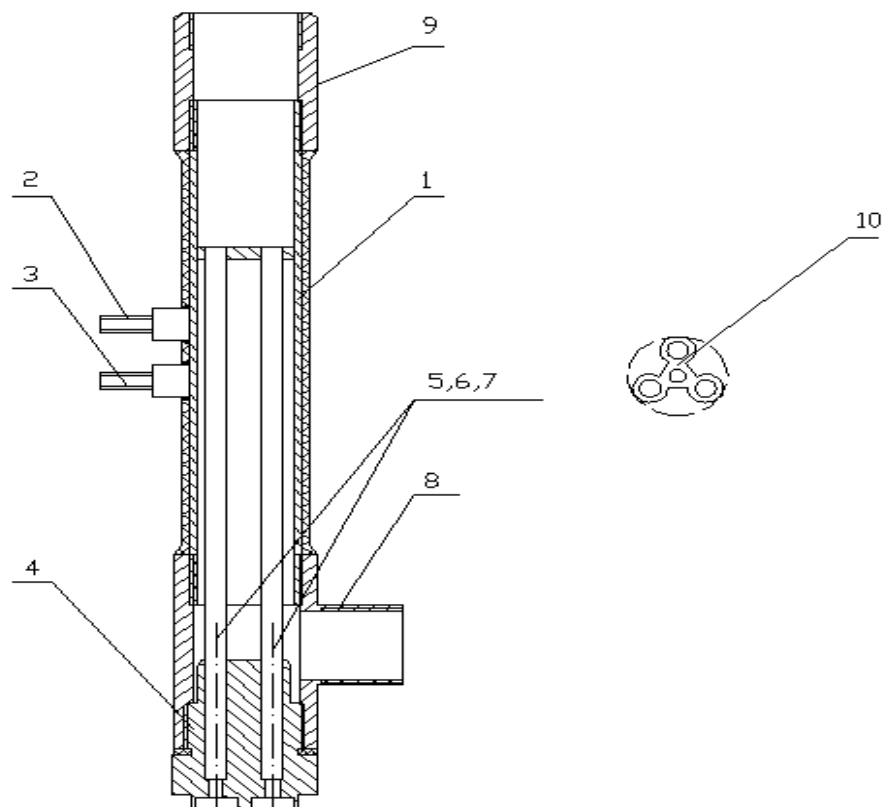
Пристрій електродний для пароутворення: 1 – корпус; 2 – нульовий контакт; 3 – заземлюючий контакт; 4 – блок фазних електродів; 5, 6, 7 – електроди; 8 – вхідний патрубок; 9 – вихідний патрубок; 10 – ізолятор
